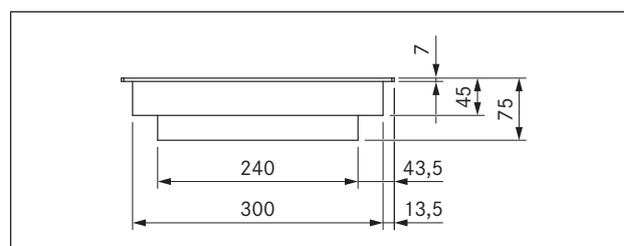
Dimensões do aparelho CKCH, vista frontal
